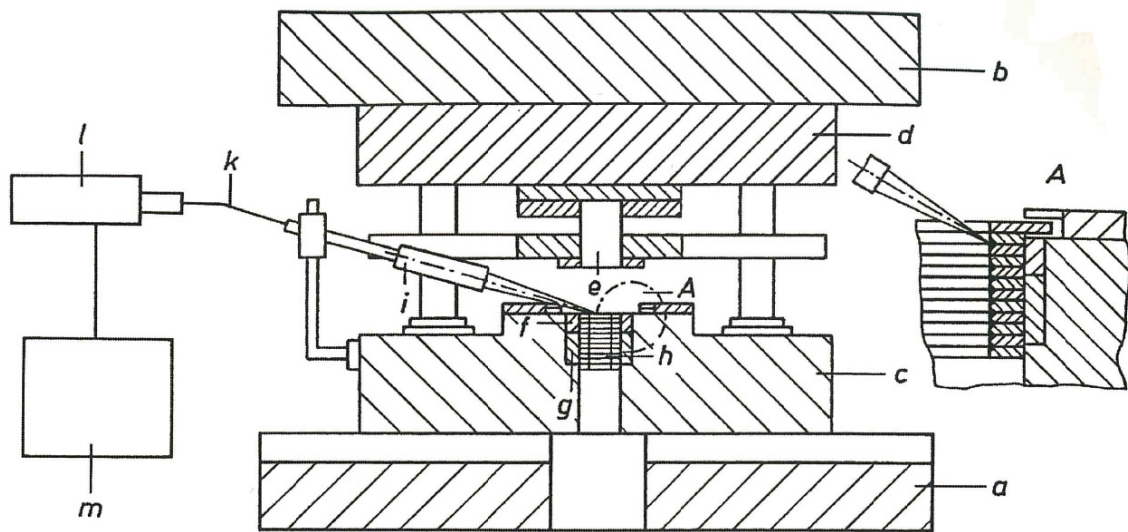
Maschine und Werkzeug für das Stanz-Laser-Paketieren, mit Ausschnitt A. a ist der Maschinentisch, b Stößel, c Unterwerkzeug, d Oberwerkzeug, e Stempel, f Matrize, g Bremse, h Paket, i Fokussiereinrichtung, k Lichtleiterkabel, l Laser, und m das Laseraggregat [20]
